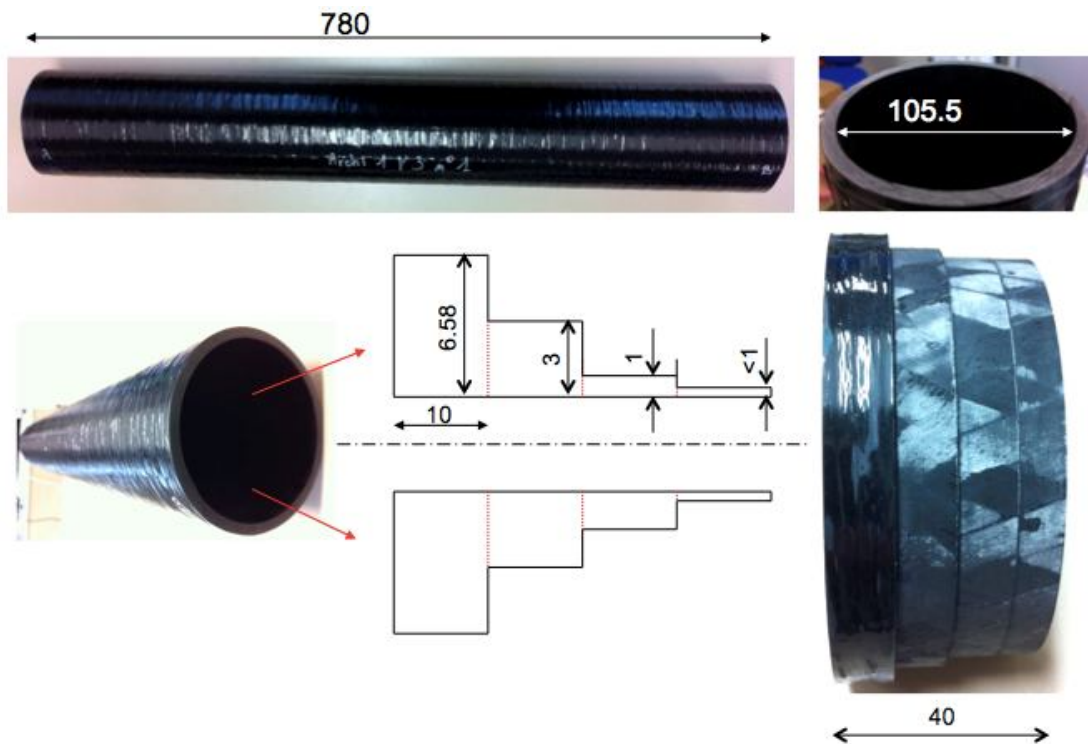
Dimensions du tube en composite et usinage d'un tronçon du tube (unitaire mm)
